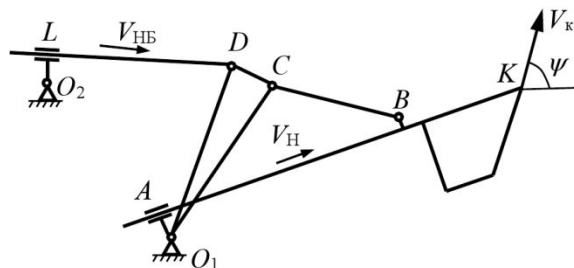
Схема передаточного механизма, соединяющие главные механизмы с ковшом:
